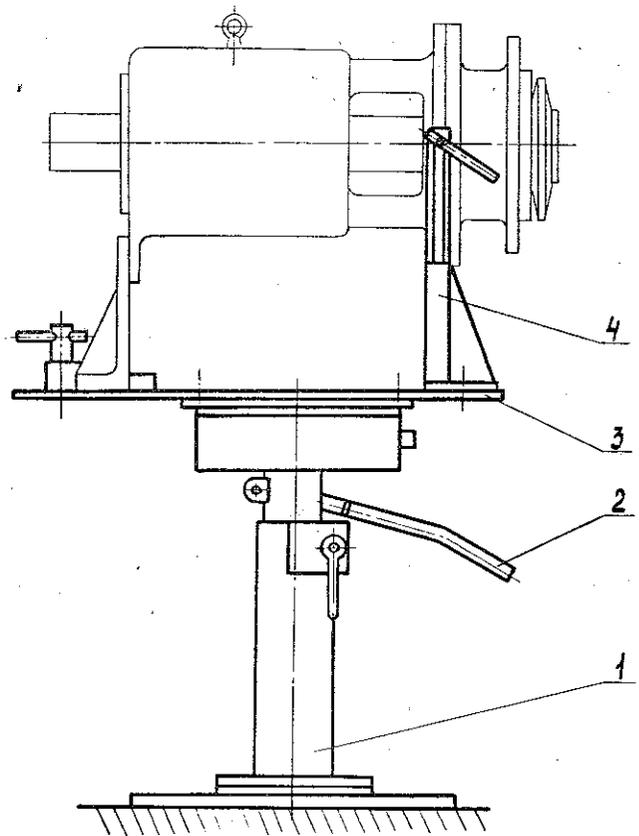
Стенд для сборки и разборки консольных насосов типа НКГ и НК
